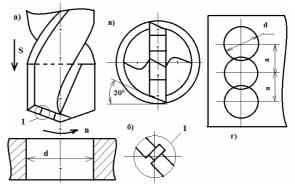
Геометрия режущей части сверла и схема резания при сверлении
